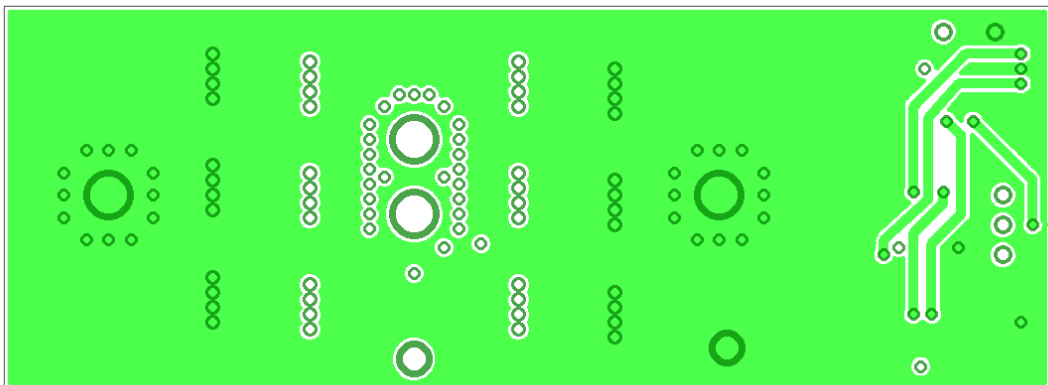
Deska plošných spojů měniče - vrstva BOTTOM
